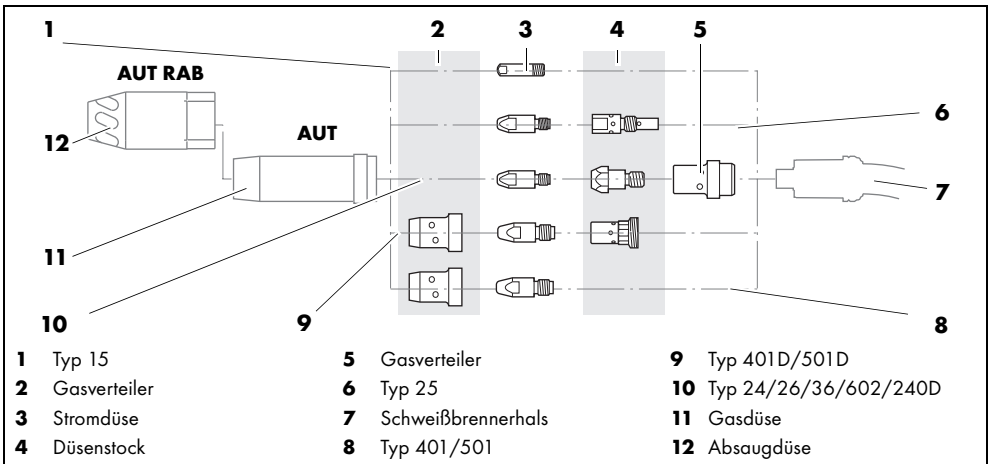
AUT / AUT RAB Schweißbrenner ausrüsten
